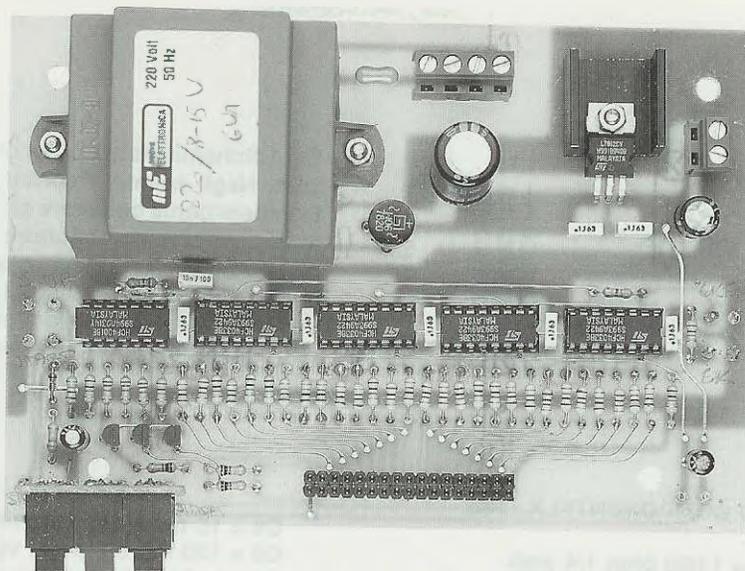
Foto dello stampato LX.1188 con sopra già montati tutti i componenti.
